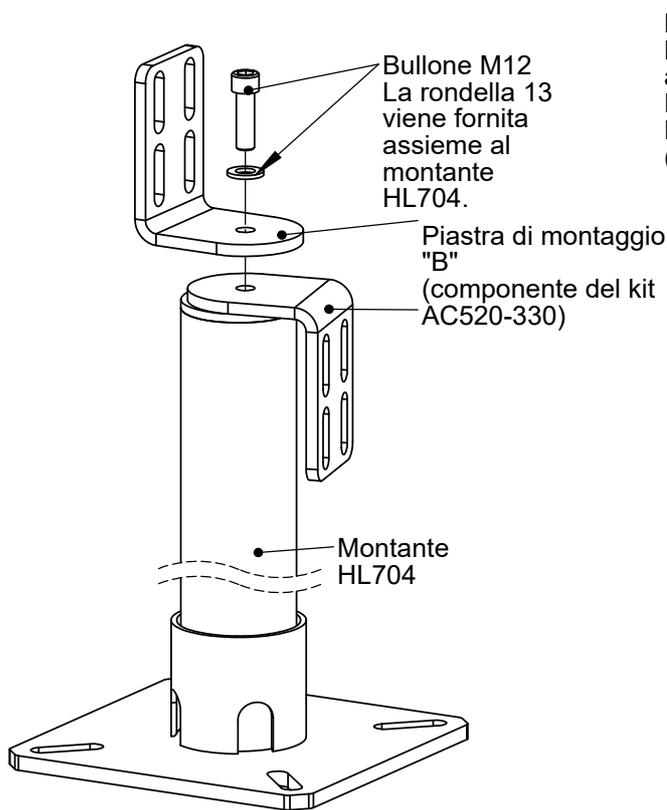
Installazione della piastra "B" sul montante HL 704.
